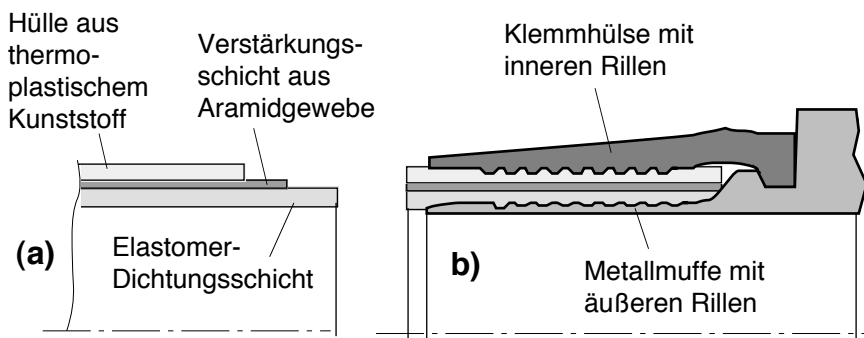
Druckschlauch für die Hydrauliktechnik (Prinzip)
